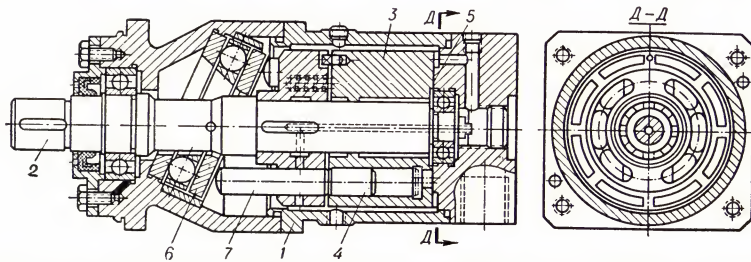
Аксиальный роторно-поршневой гидромотор: 1 — корпус; 2 — вал; 3 — ротор; 4 — поршень; 5 — распределительный диск; 6 — наклонная шайба; 7 — толкатель.
